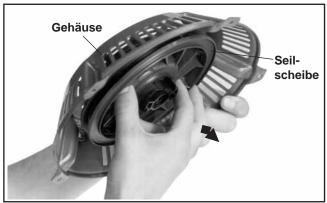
Seilscheibe aus dem Gehäuse entfernen.
